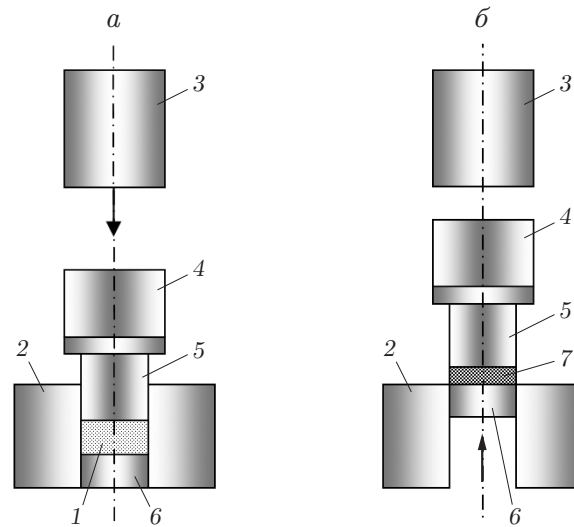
Схема установки для прессования порошка СВМПЭ:
